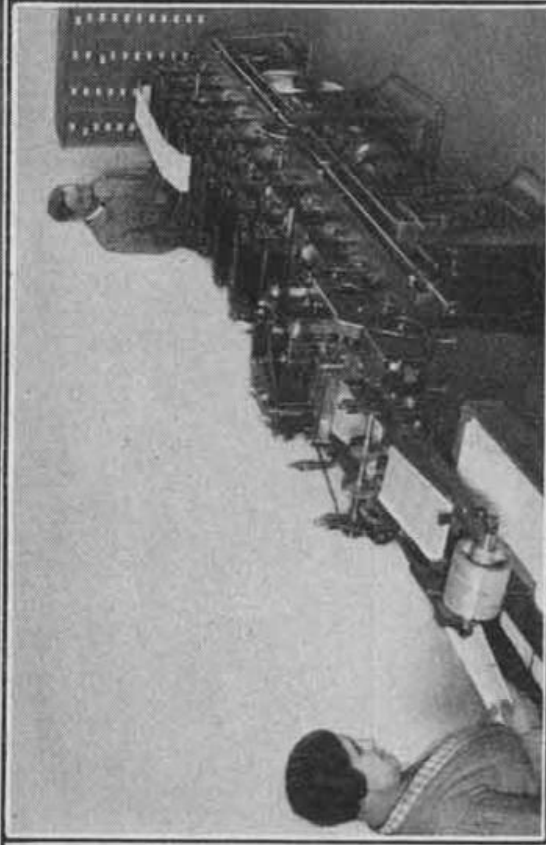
Machine rotative à imprimer les billets passe-partout avec souche.
